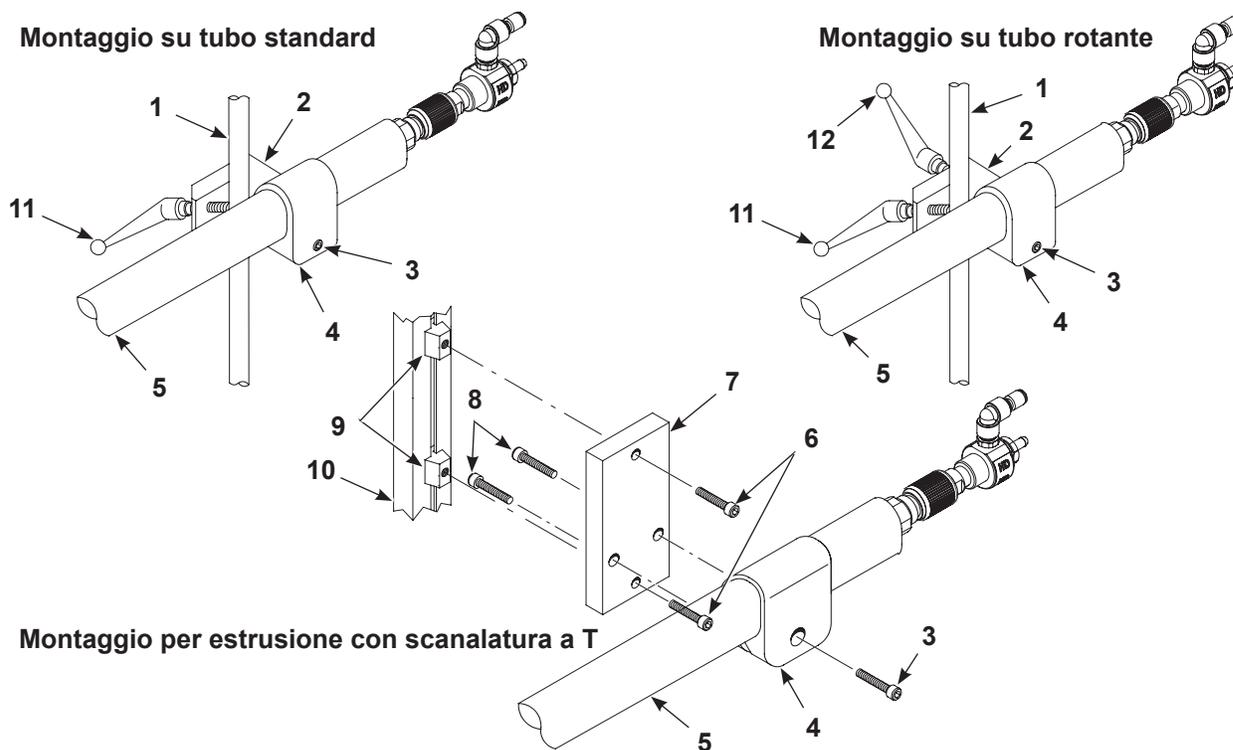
Gruppi di montaggio della pistola a spruzzo con montaggio su tubo
